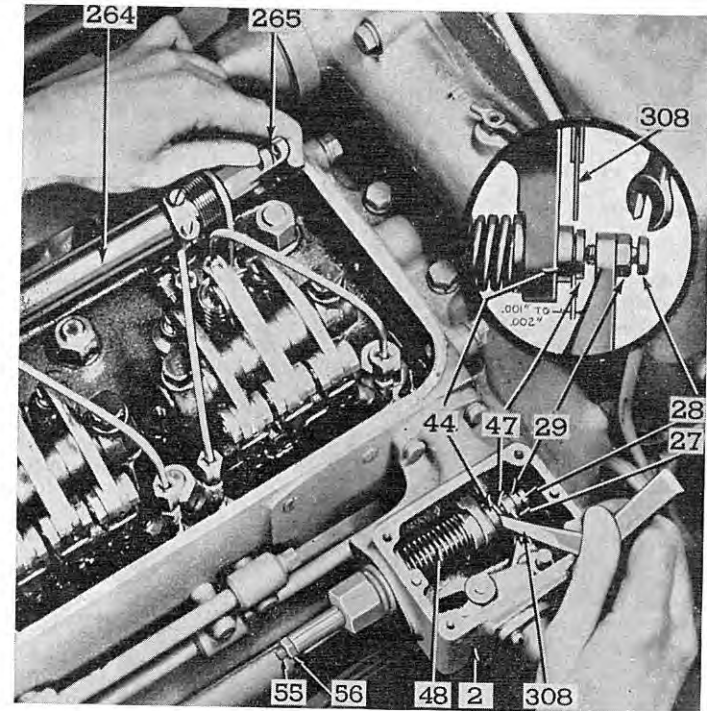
Réglage du jeu du régulateur (DW-LS)
